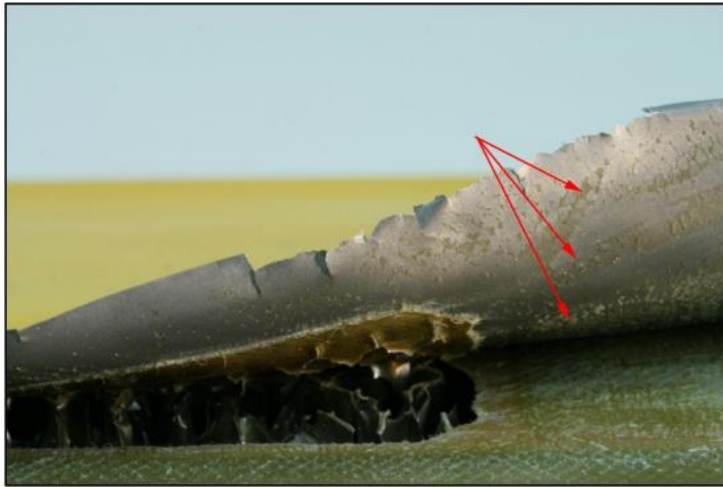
Detalle de delaminación, las flechas rojas indican secciones donde el pegamento no había sido aplicado correctamente.
